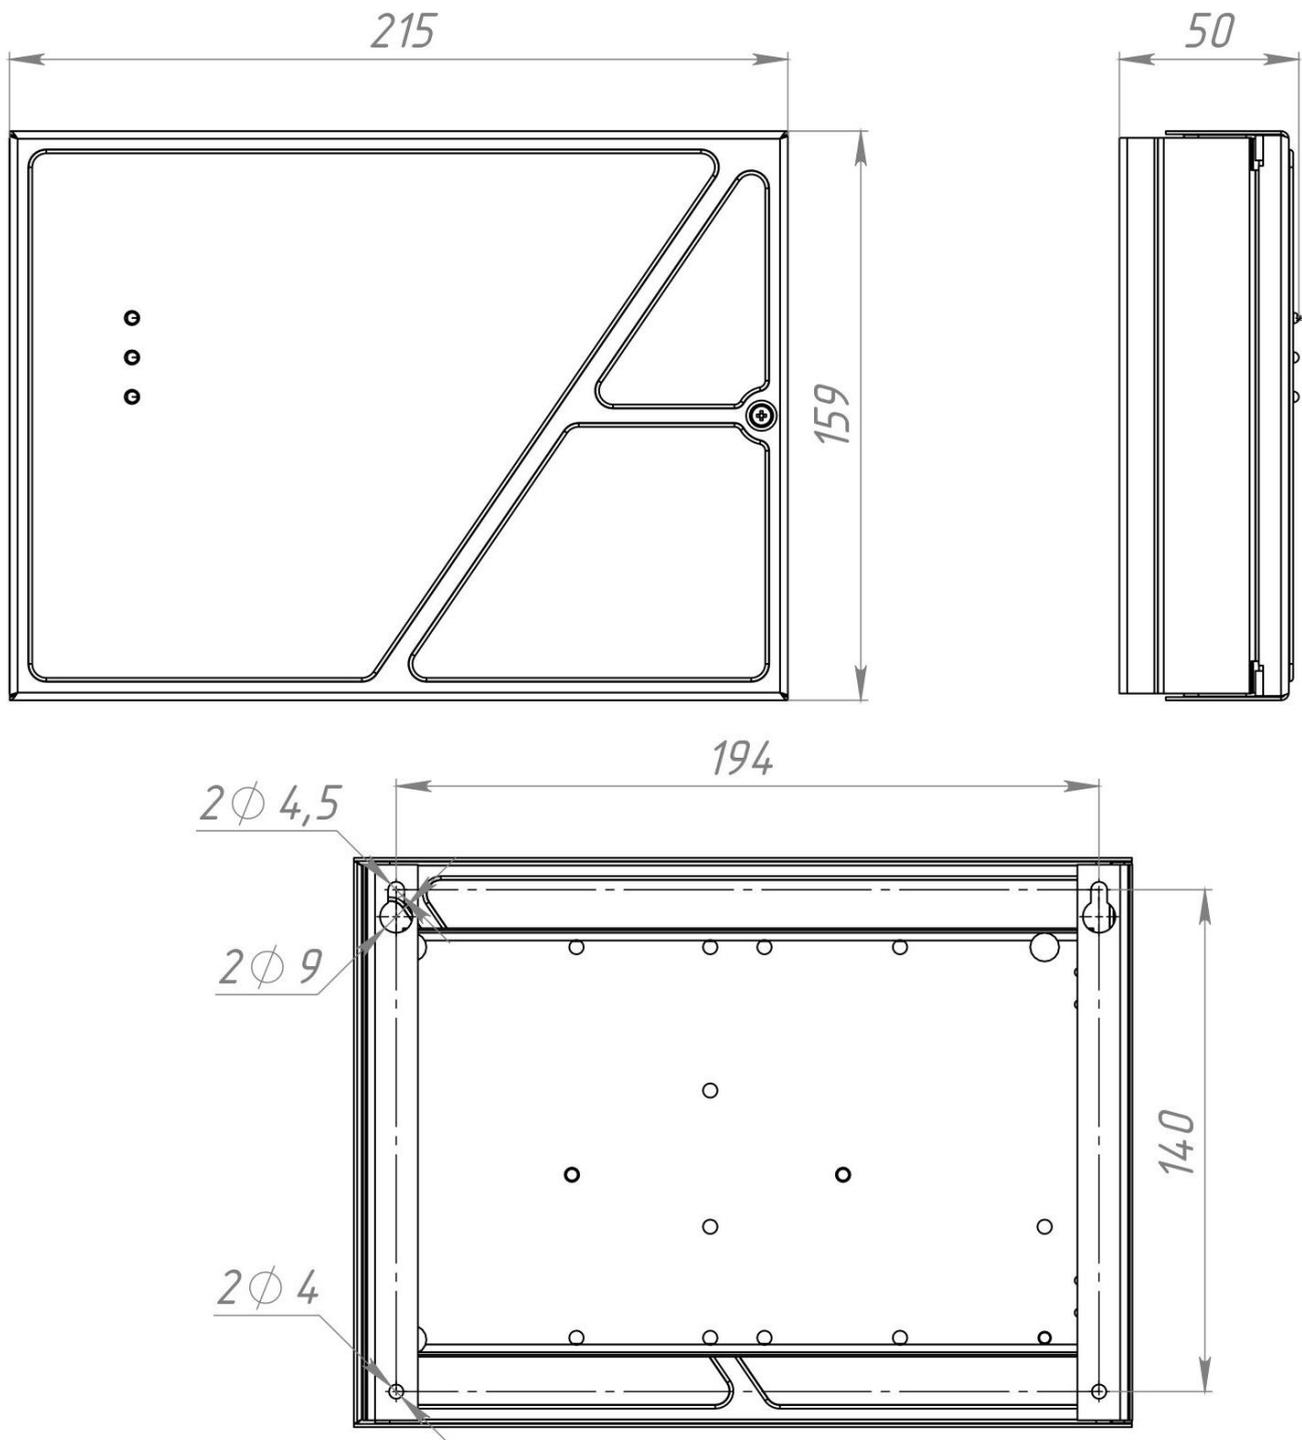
Габаритные и установочные размеры ШИМР-16
